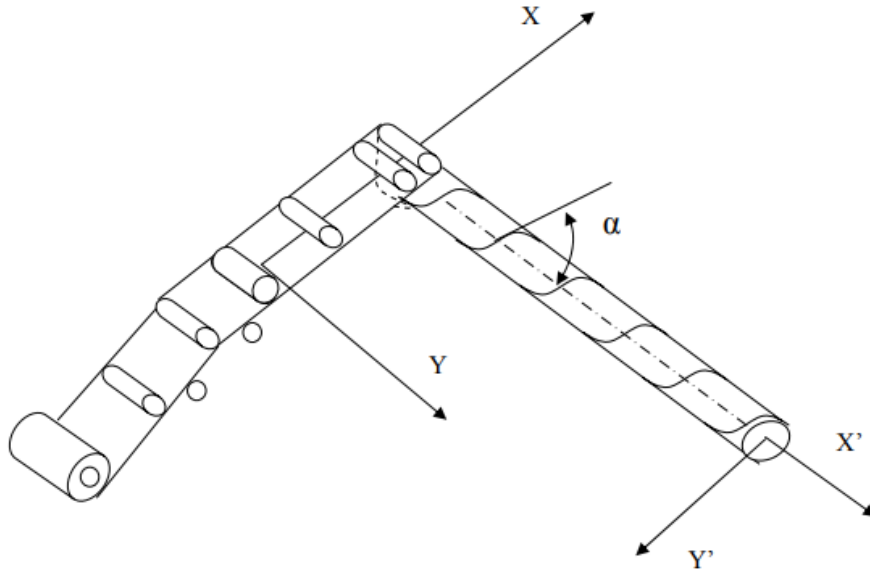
Principe de fabrication des tubes soudés
